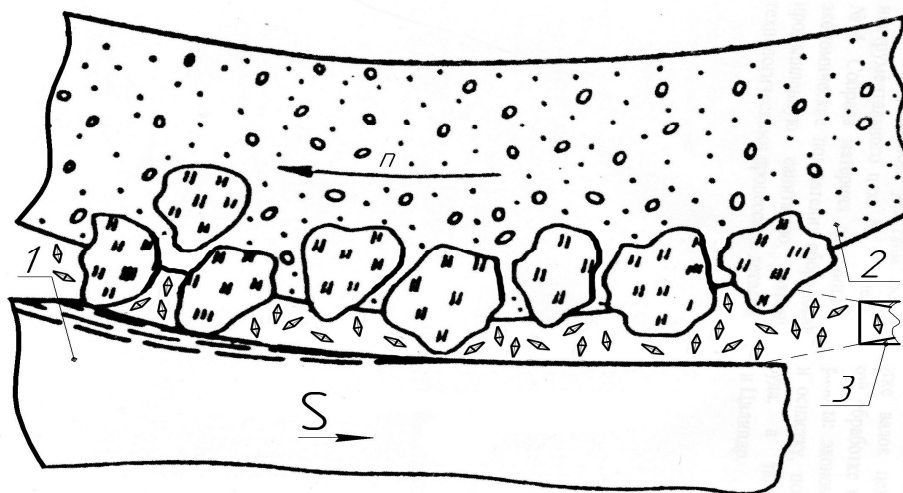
Схема шлифования с гидроабразивной обработкой.
